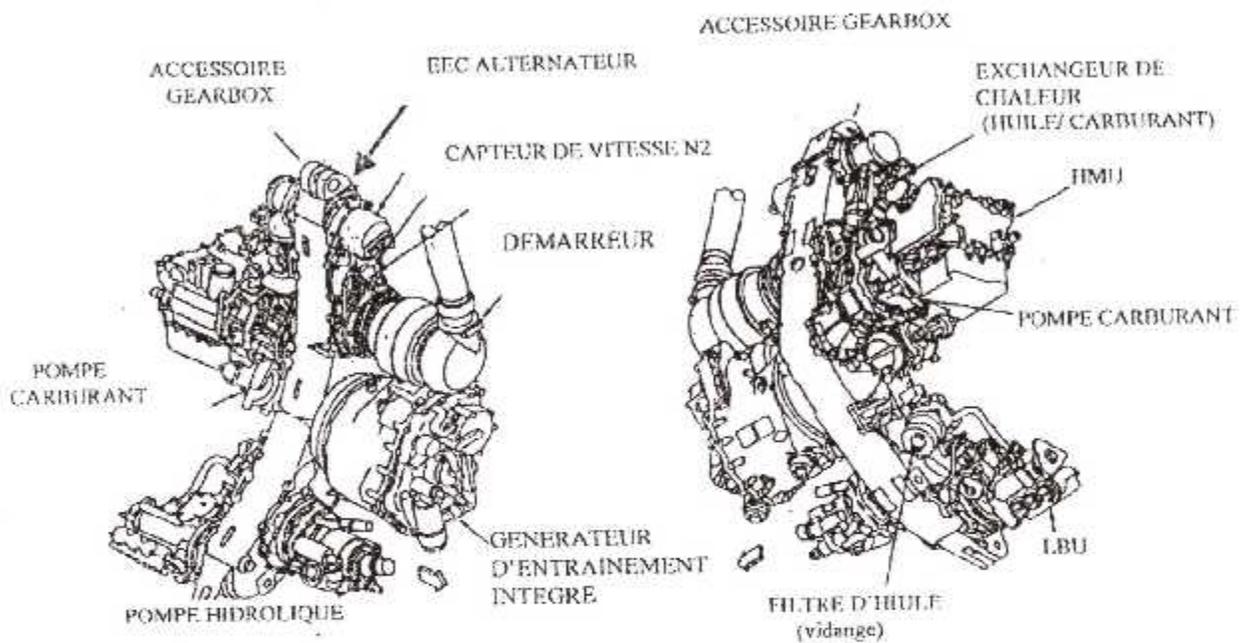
Vue Avant et Arrière de l'AGB.
